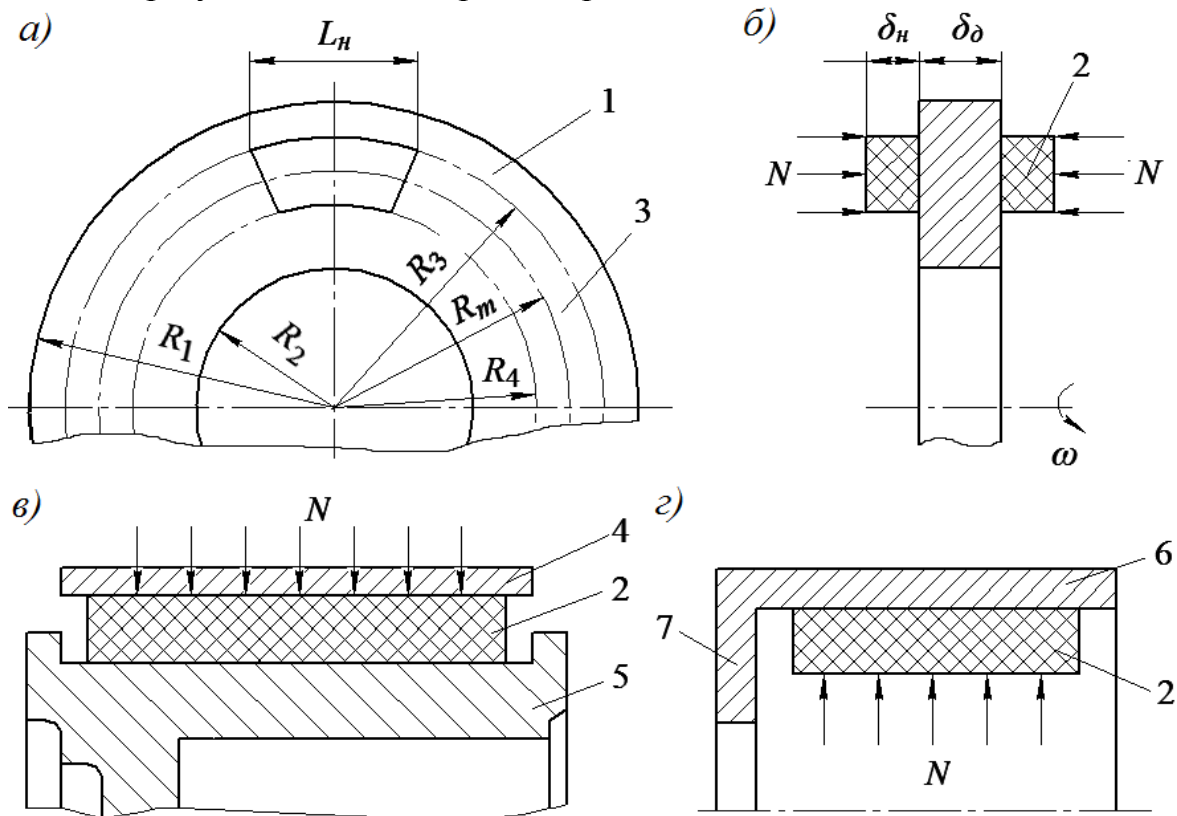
а, б, в, г – Схемы различных типов фрикционных узлов тормозных устройств: а, б – дисково-колодочного (продольный и поперечный разрез); в – ленточно-колодочного (поперечный разрез); г – барабанно-колодочного (поперечный разрез)
